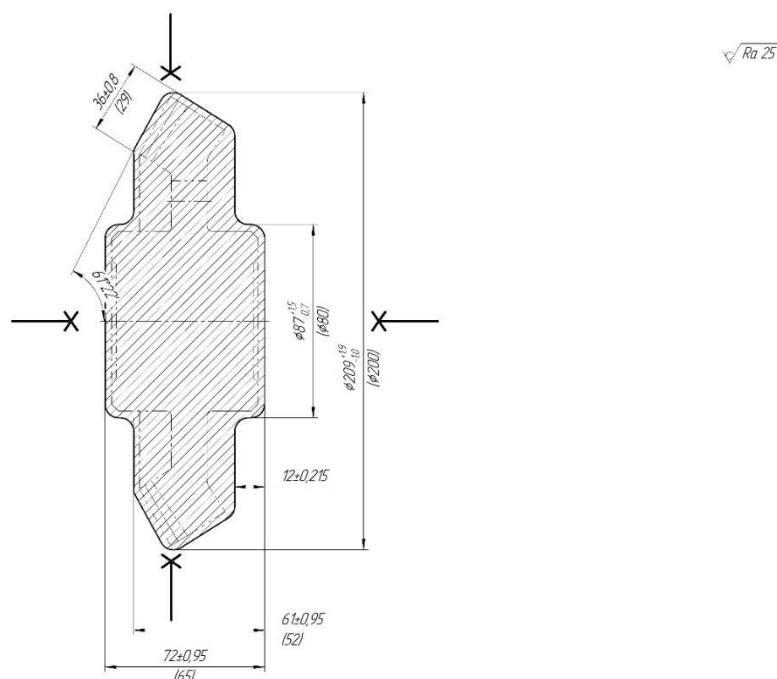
Ескіз заготовки, яка отримана штамповкою на ГKM
